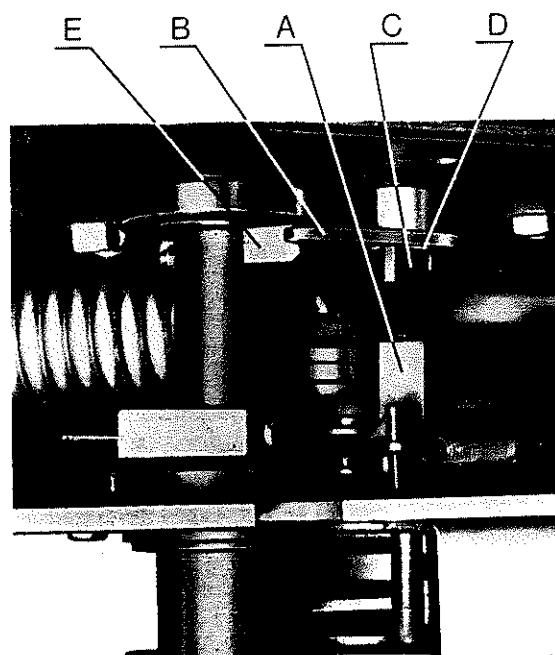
Montaggio dispositivo di sgancio per sganciatori esterni
